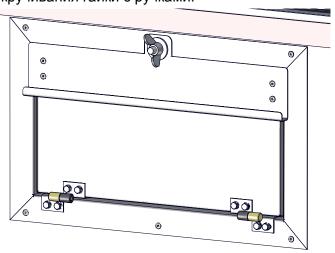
Внешний вид жалюзи двери в закрытом положении
